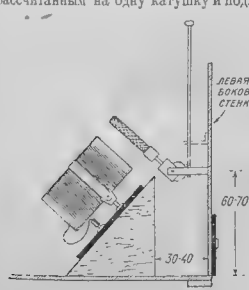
Крепление катушки L_1 и устройство подвижного станочка для катушки обратной связи.
